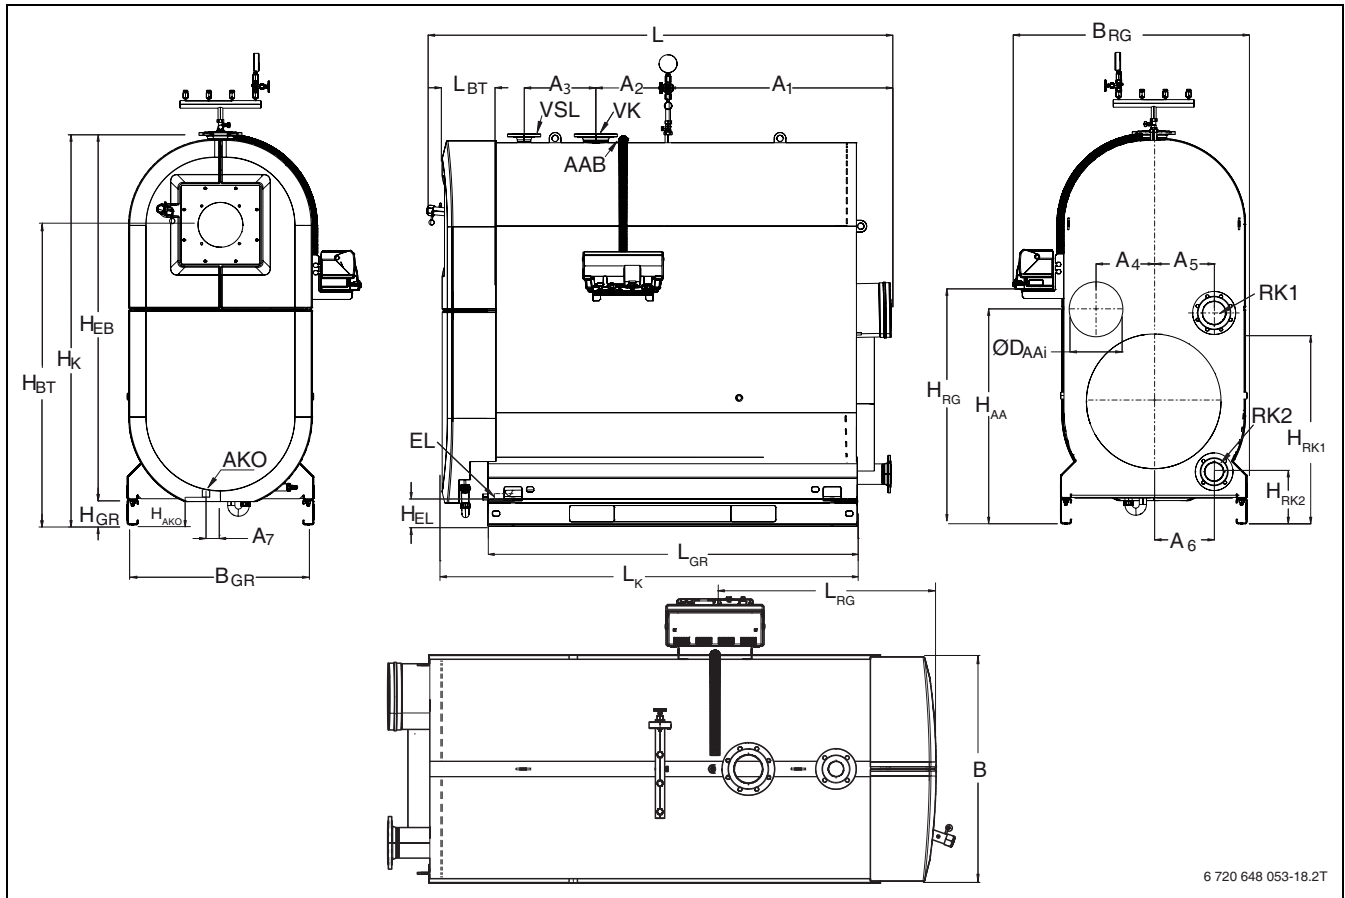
Dimensioni caldaia 800 kW, 1000 kW, 1200 kW
